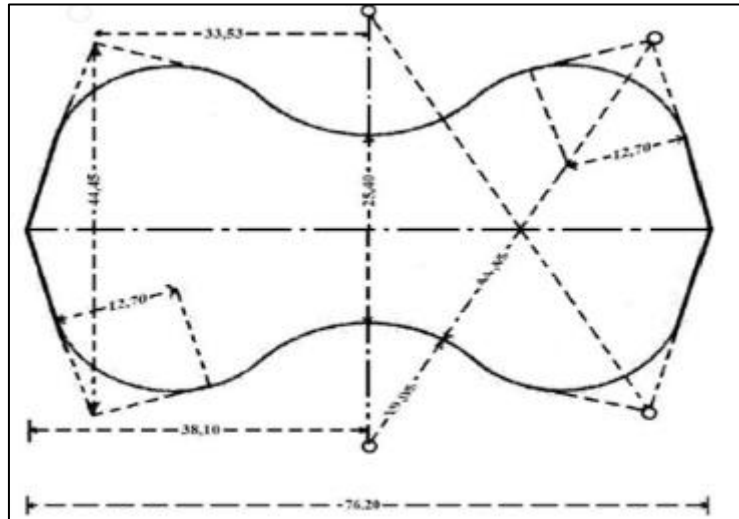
Dimensiones del molde para el ensayo de resistencia a la tracción
